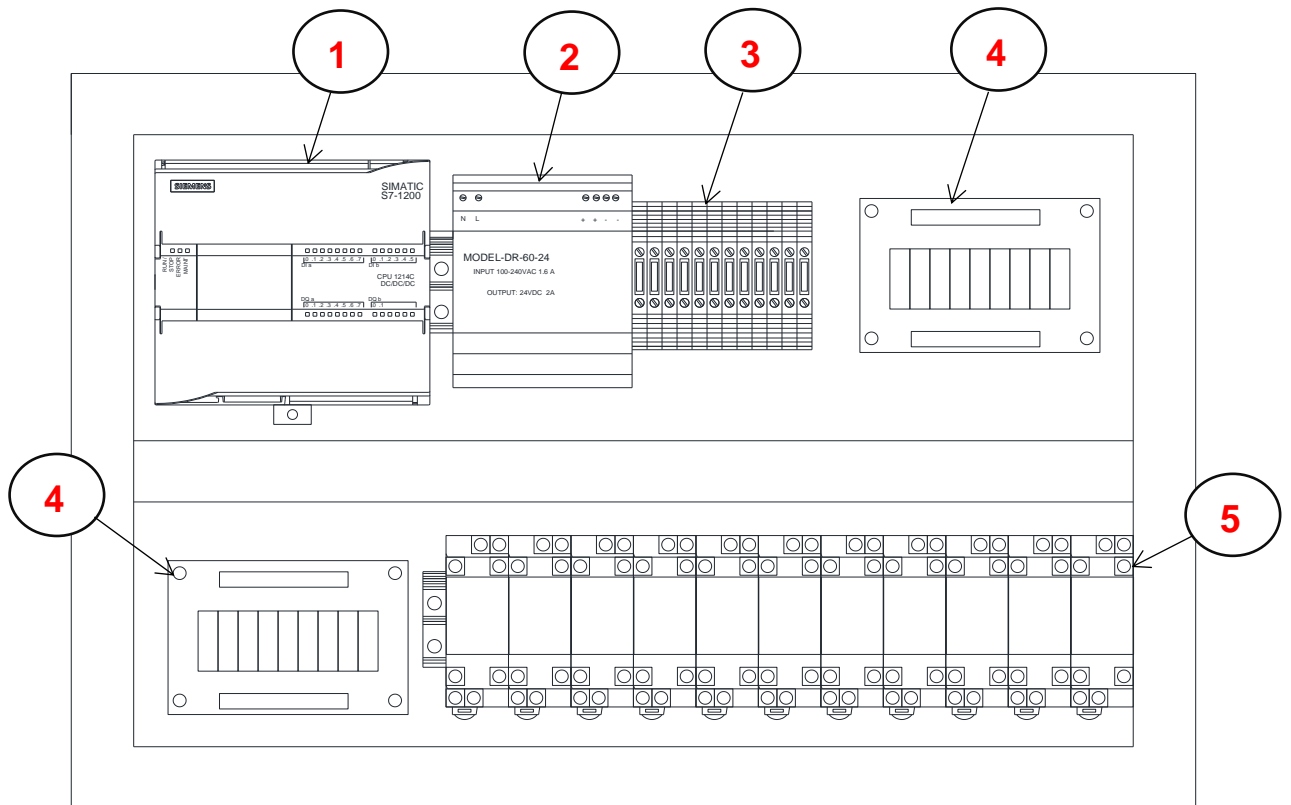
Disposición de elementos sobre el plafón, diseño en AutoCAD.
